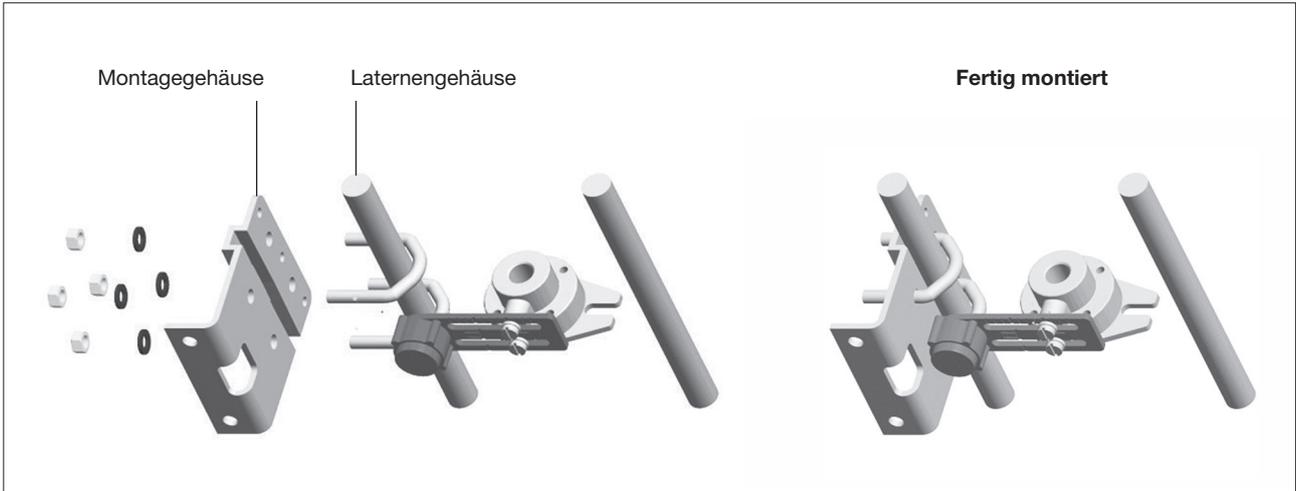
Montage Montageplatte an Linearantriebe mit Säule
